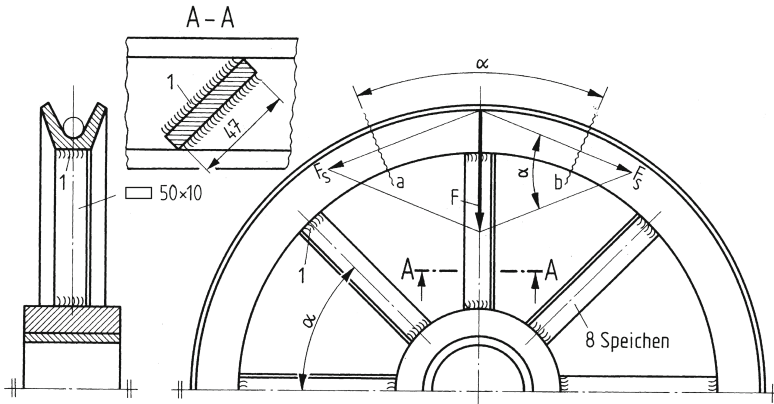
Seilrolle mit eingeschweißten Speichen
